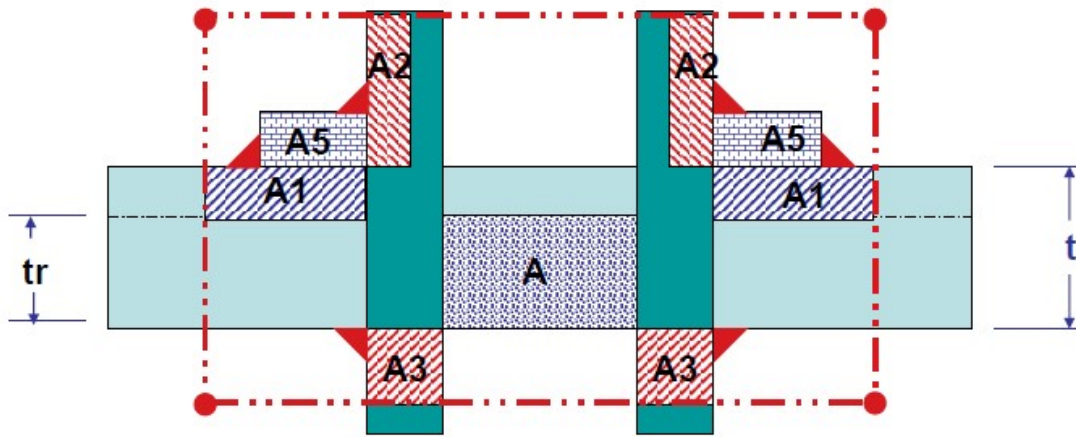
Vista de corte de la unión boquilla estanque, con refuerzos y soldadura [3]
